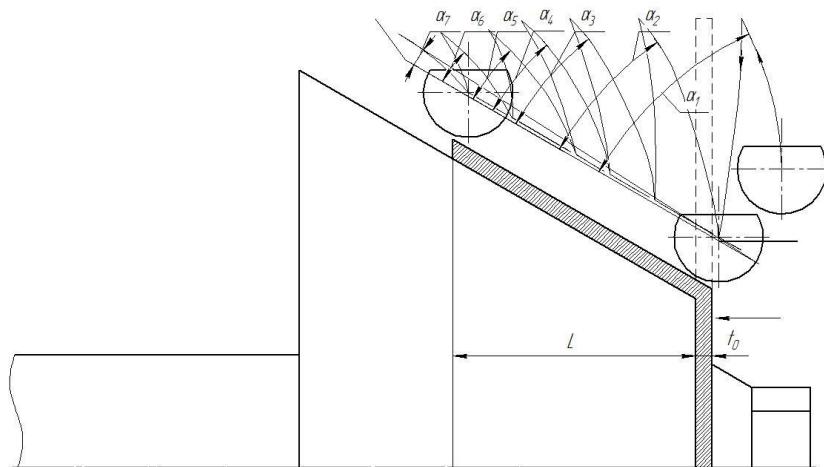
Послідовність ротаційної витяжки заготовки траекторії руху інструмента
